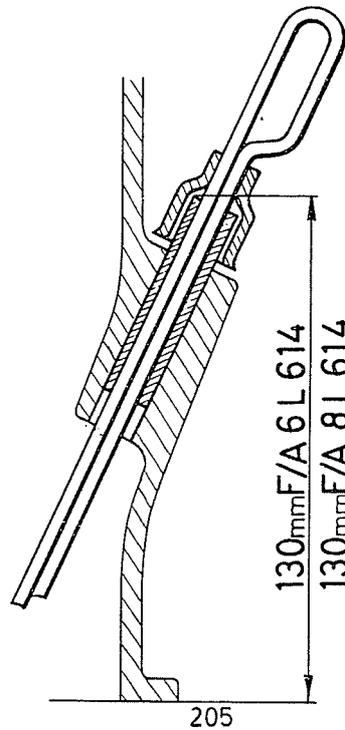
Einbau des Führungsrohres zum Ölpeilstab F/A 6-8L 614
